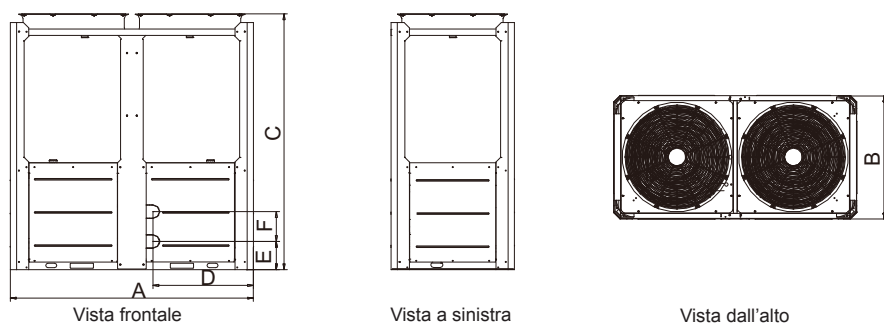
Dimensione d'insieme di KEM-90 DRS5
